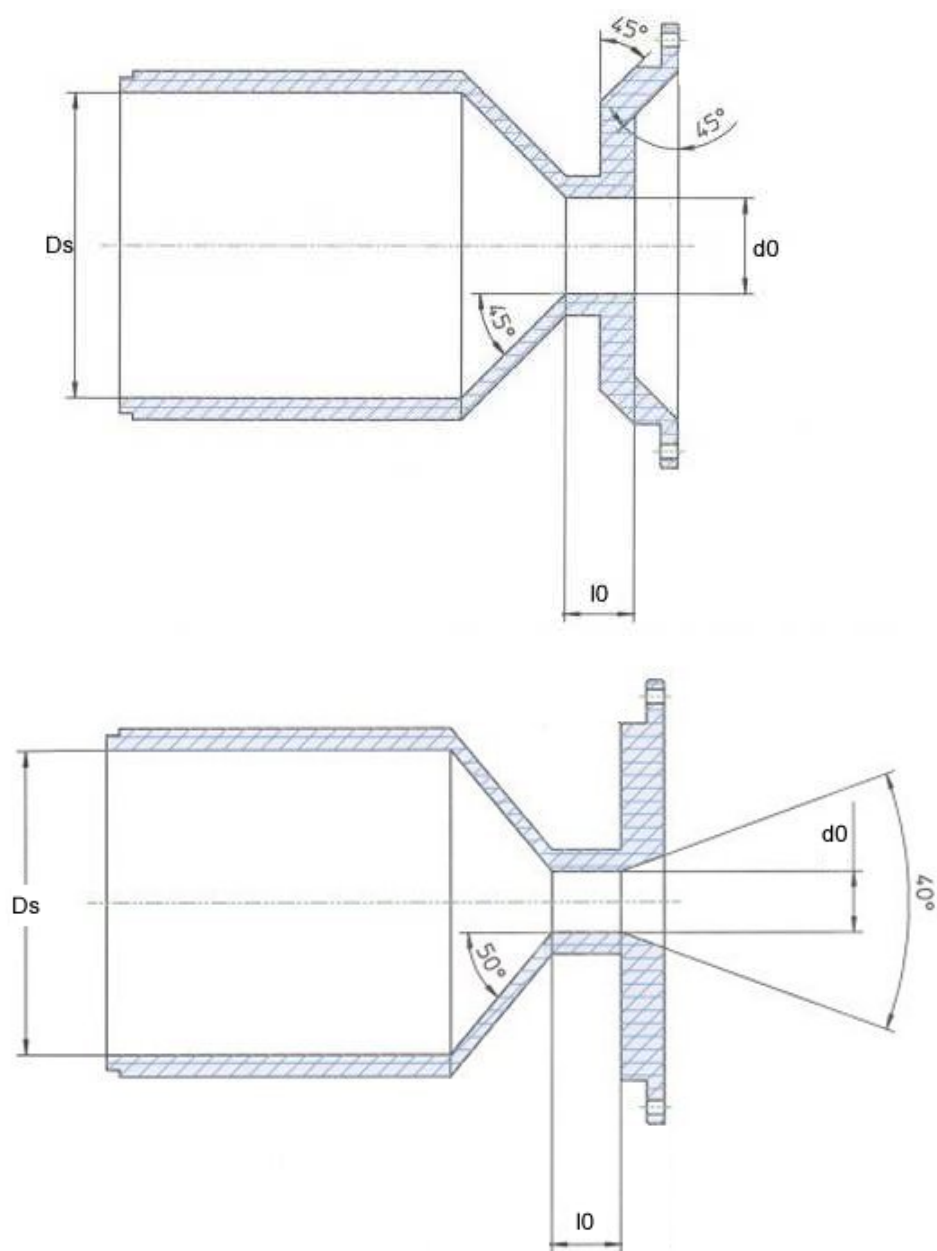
Plans des embouts n°2 (en haut) et n°4 (en bas)
